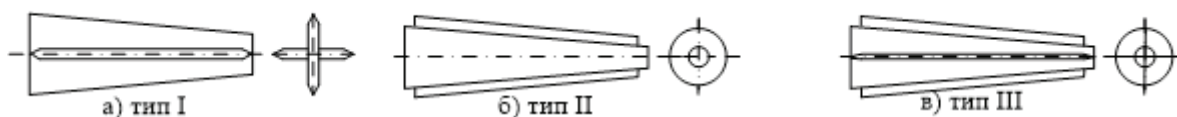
Успокоители потоков: а) крестообразный; б) радиально-трубчатый; в) радиально-трубчатый с пересекающимися пластинами
